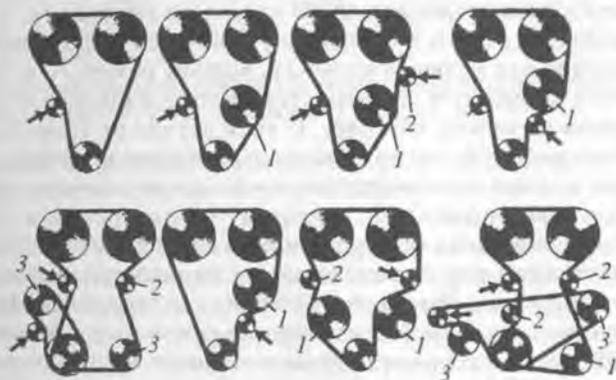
Основные схемы ременного привода распределительного механизма с двумя верхними валами
